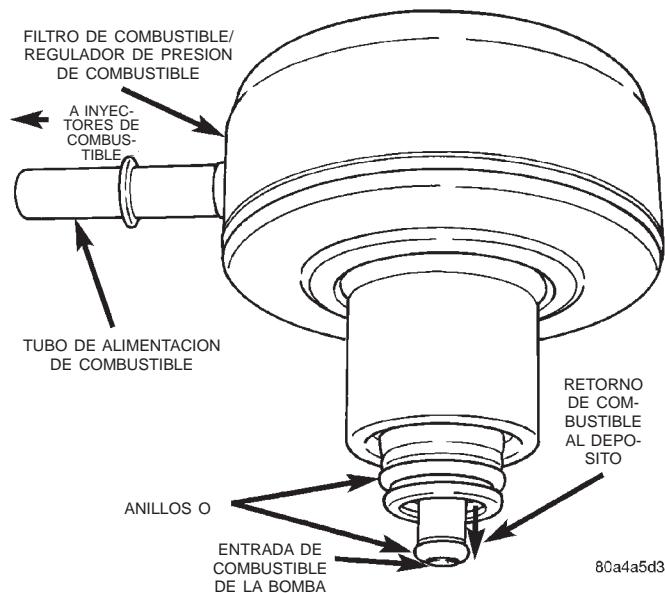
Anillos O del filtro de combustible/regulador de presión de combustible
